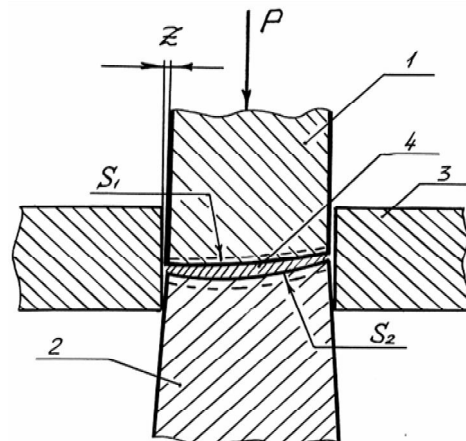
Схема изотермической штамповки детали типа «лопатка»: 1-пуансон; 2-матрица; 3-рамка; 4-деталь штампуемая.
